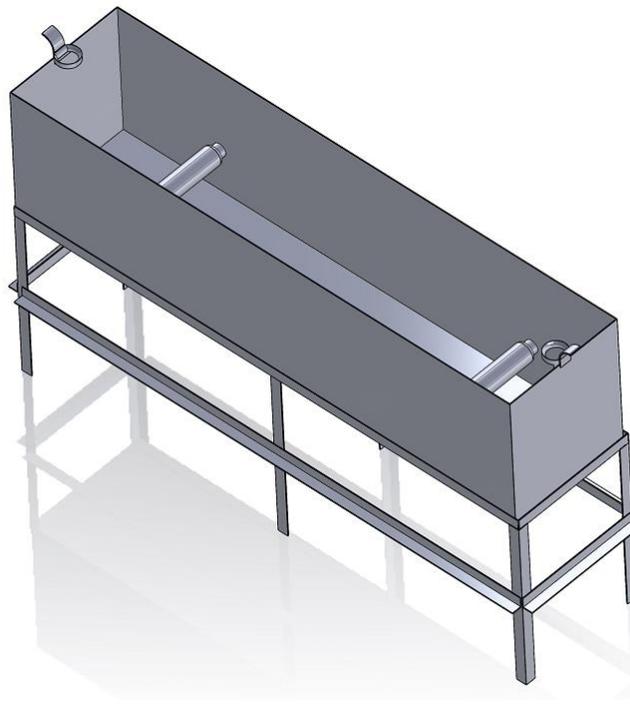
Diseño isométrico del módulo de coagulado: tanque de enfriamiento.
